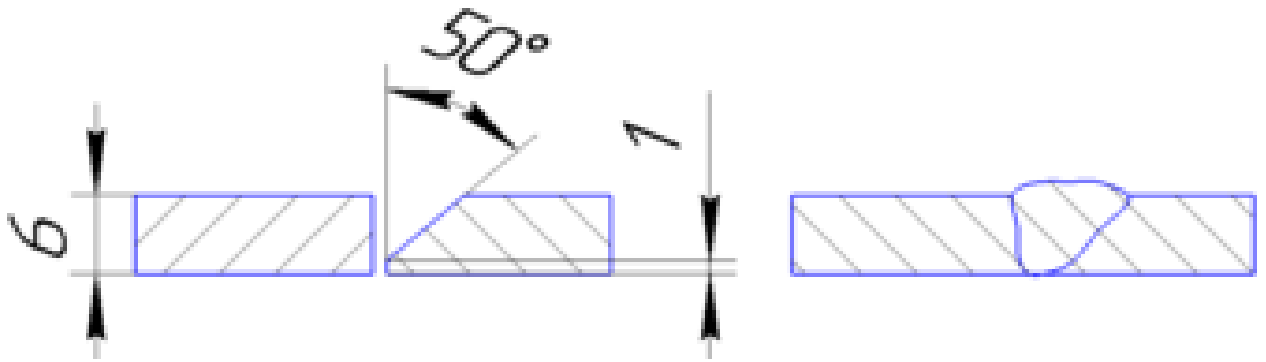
Общий вид соединения С8, сборка и сварка
